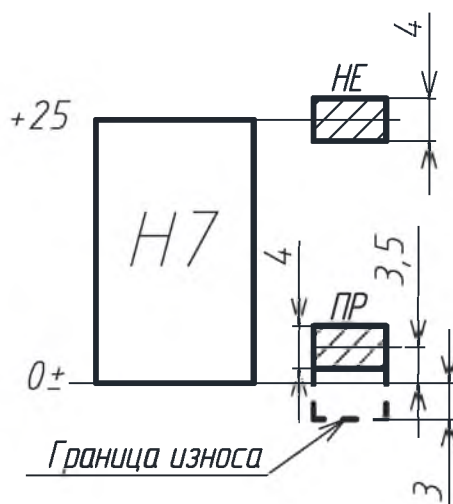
Схема расположения полей допусков рабочих калибров $\varnothing 40H7$
